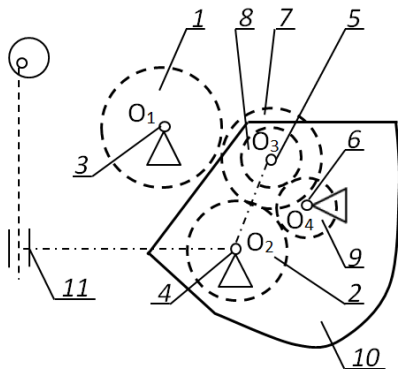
Схема дробилки с межвалковой зубчатой передачей
